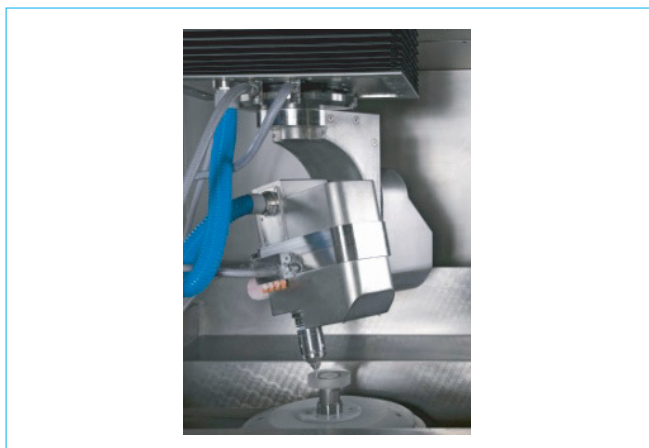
Outil AFJP dans machine CN (source : Optotech)
